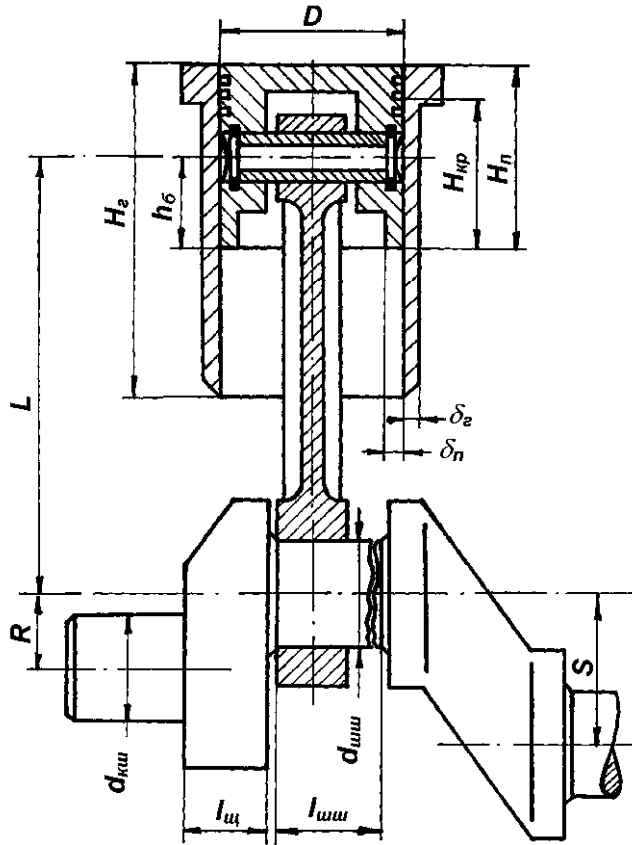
Шатунно-поршнева група непрямоточного компресора і фрагмент валу
